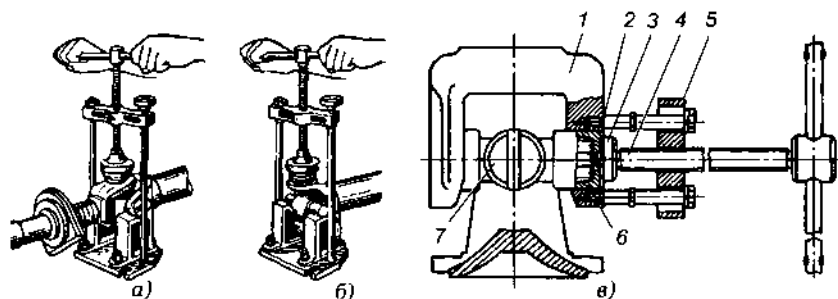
Разборка карданного шарнира с помощью универсального съемника: а — выпрессовка подшипников из скользящей вилки; б — выпрессовка подшипников из вилки карданного вала; в — разборка карданного вала автомобиля марки «КамАЗ»; 1 — вилка; 2 — установочный болт; 3 — пята; 4 — винт съемника; 5 — поперечина; 6 — стакан; 7 — крестовина
